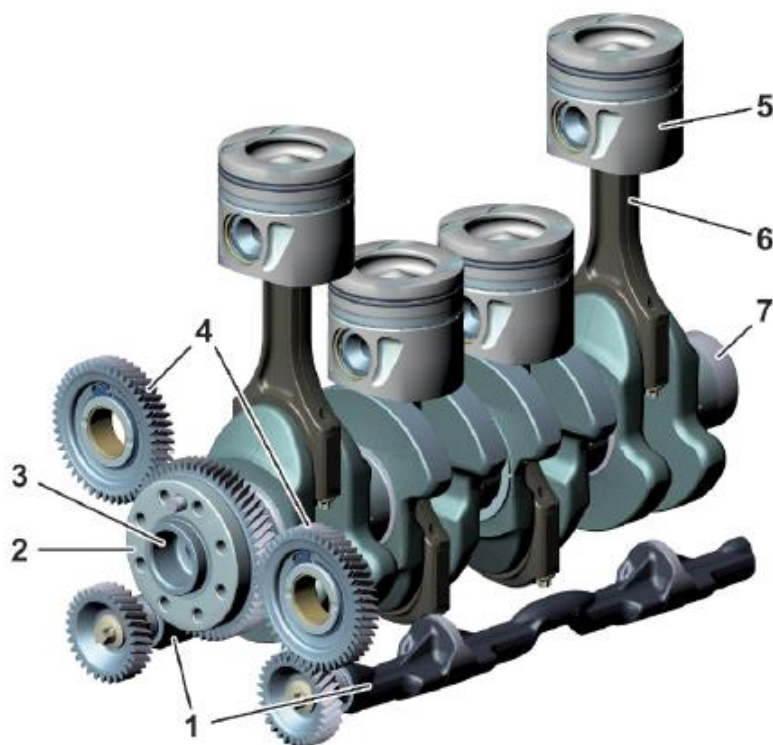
Кривошипно-шатунный механизм и привод вспомогательных механизмов: 1 – балансирующие валы Ланчестера; 2 – приводная шестерня; 3 – коленчатый вал; 4 – промежуточные шестерни; 5 – поршень; 6 – шатун; 7 – торсионный гаситель крутильных колебаний
